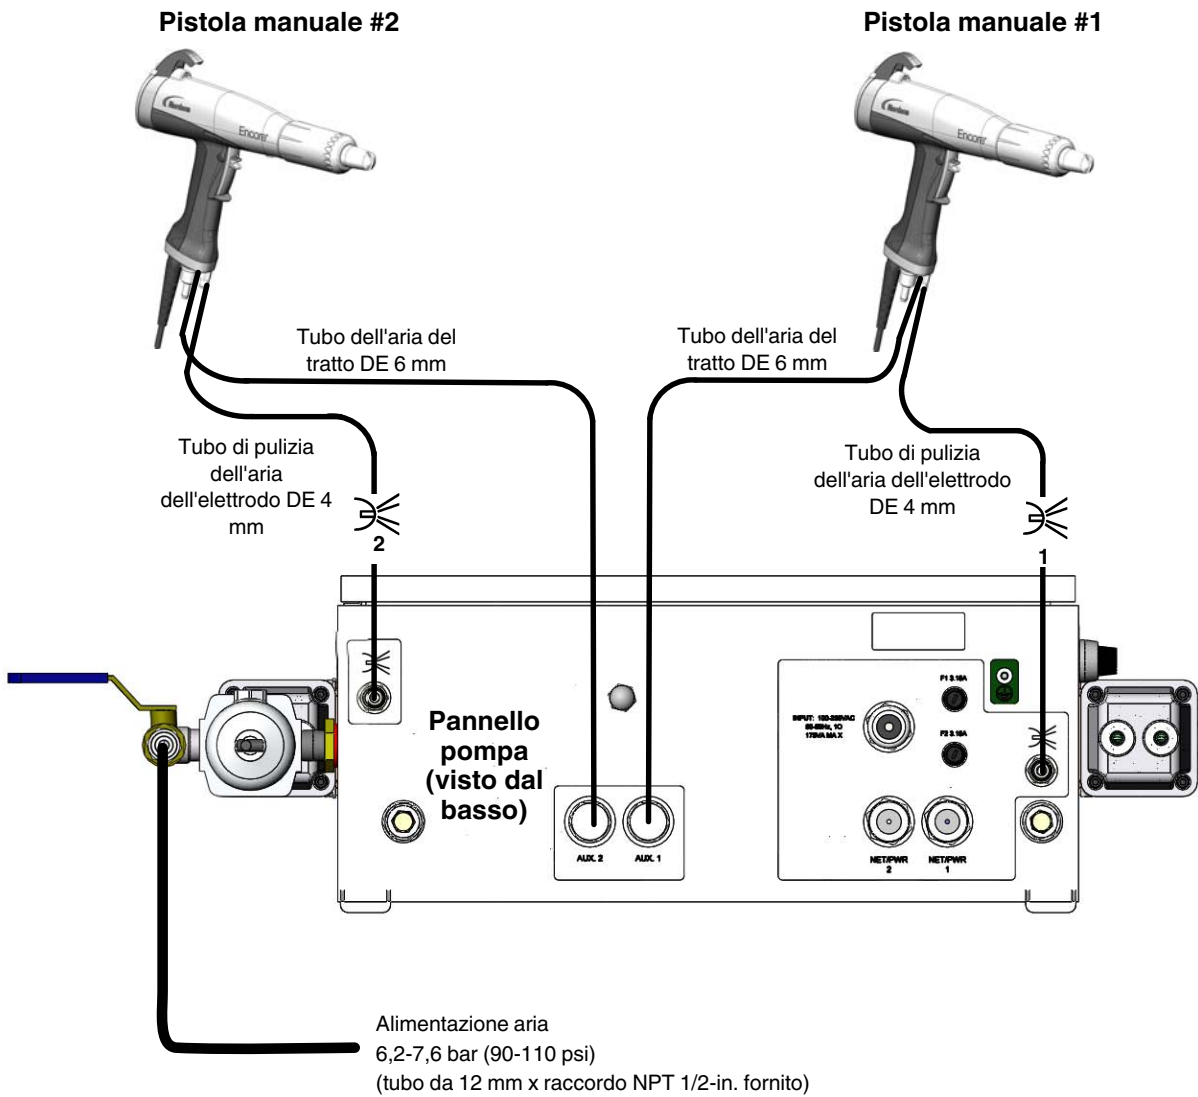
Collegamenti di alimentazione d'aria al sistema e dell'aria della pistola
